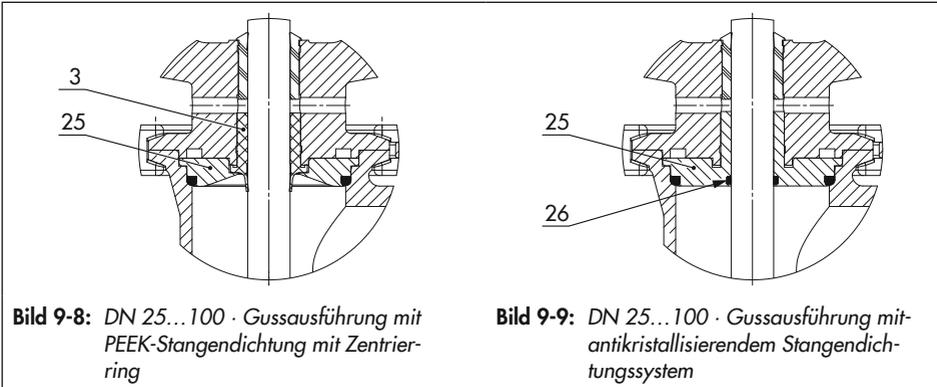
DN 25...100 · Gussausführung mit PEEK-Stangendichtung mit Zentrier-ring
